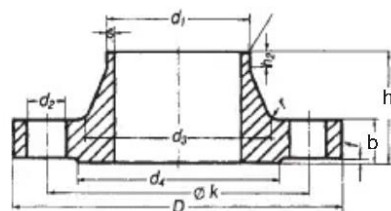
Esquema para el diseño y dimensionamiento de las bridas de cuello soldable. Fuente: (GRUPO HASTINIK, 2002, pág. 36).
